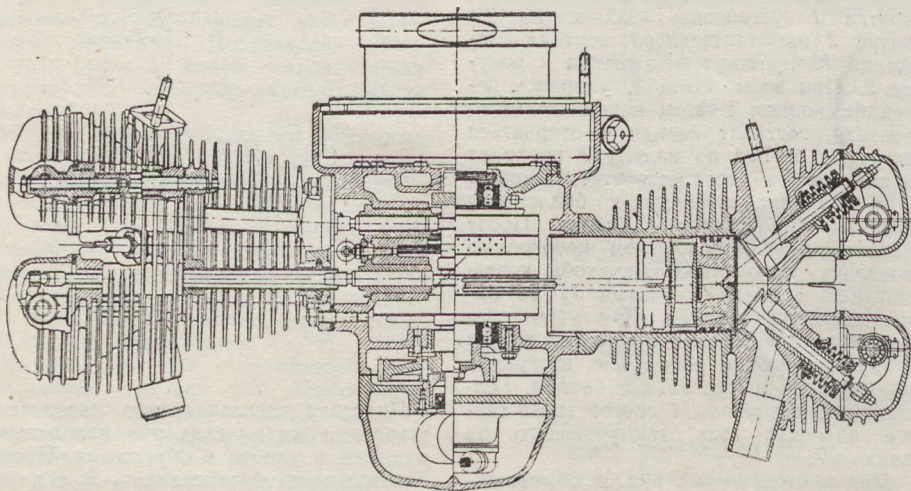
Двигатель мотоцикла М-75. Вид сверху.
